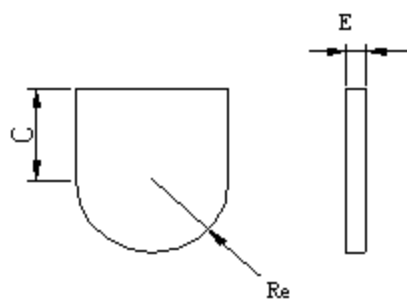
Seccionamiento de las tapas de la canal 1. Fuente. Propia.
